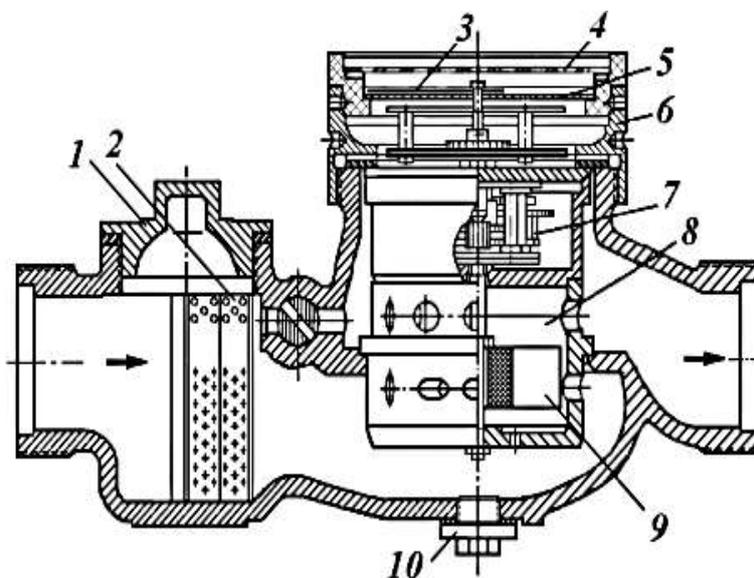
Дозатор воды турбинного типа: 1 – корпус; 2 – сетка; 3 – стрелка; 4 – стекло; 5 – циферблат; 6 – поворотное кольцо; 7 – редуктор; 8 – камера крыльчатки; 9 – крыльчатка; 10 – пробка
